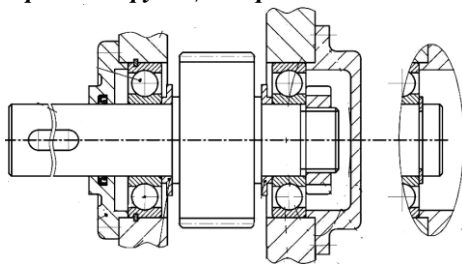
Вал-шестерня с 2-мя подшипниками
